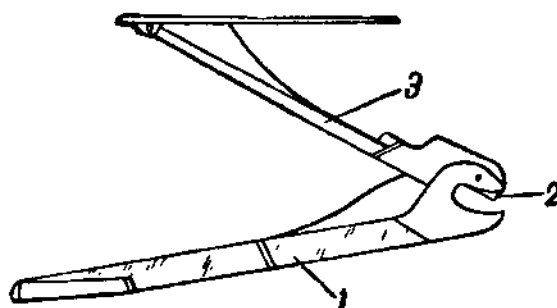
Крышка магази́нной коробки с подающим механизмом:
